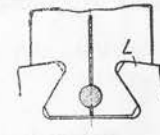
Coadă de rândunică cu fixare printr'un bolț de despicare.
